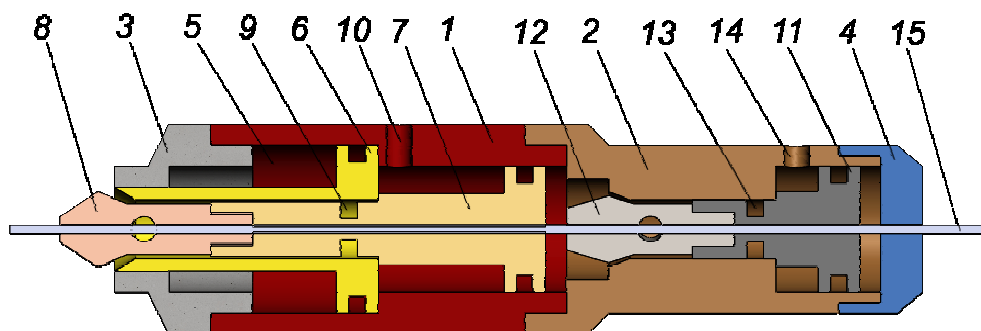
Схема наплавочной головки с импульсной подачей проволоки:
